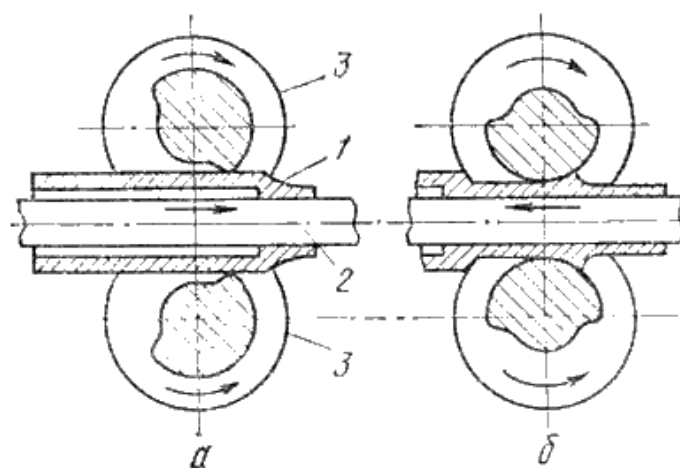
Схема прокатки труб на пилигримовом стане:
